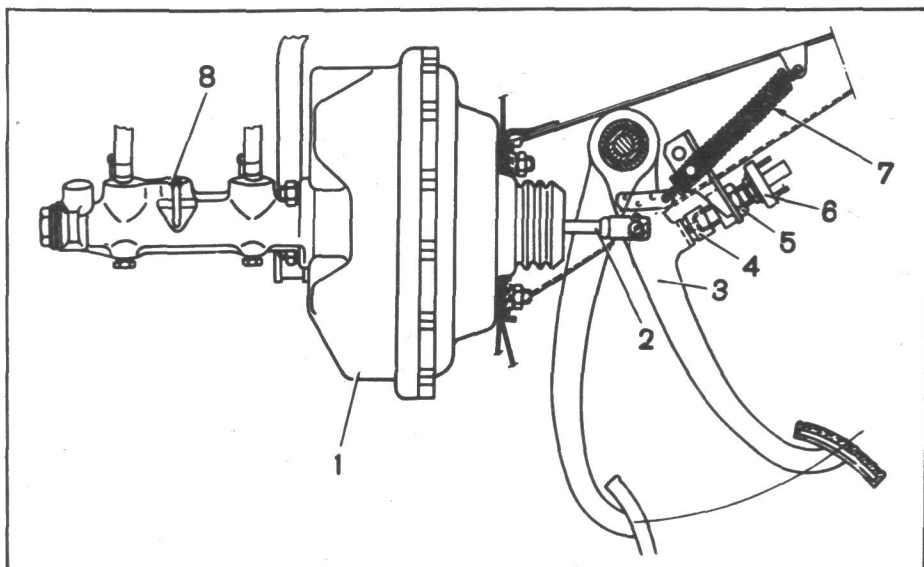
Педаль тормоза: 1 — вакуумный усилитель; 2 — толкатель; 3 — педаль тормоза; 4 — буфер выключателя стоп-сигнала; 5 — гайка упорного винта; 6 — выключатель стоп-сигнала; 7 — оттяжная пружина педали; 8 — главный цилиндр гидросистемы тормозов
